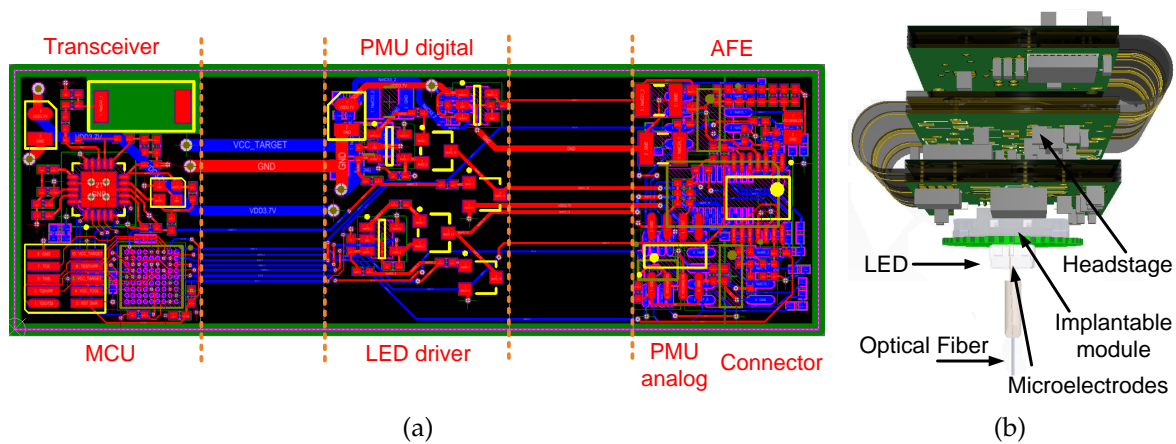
a) Design du PCB flexible rigide, b) vue 3D du PCB flexible rigide replié et connecté à un module implantable.
